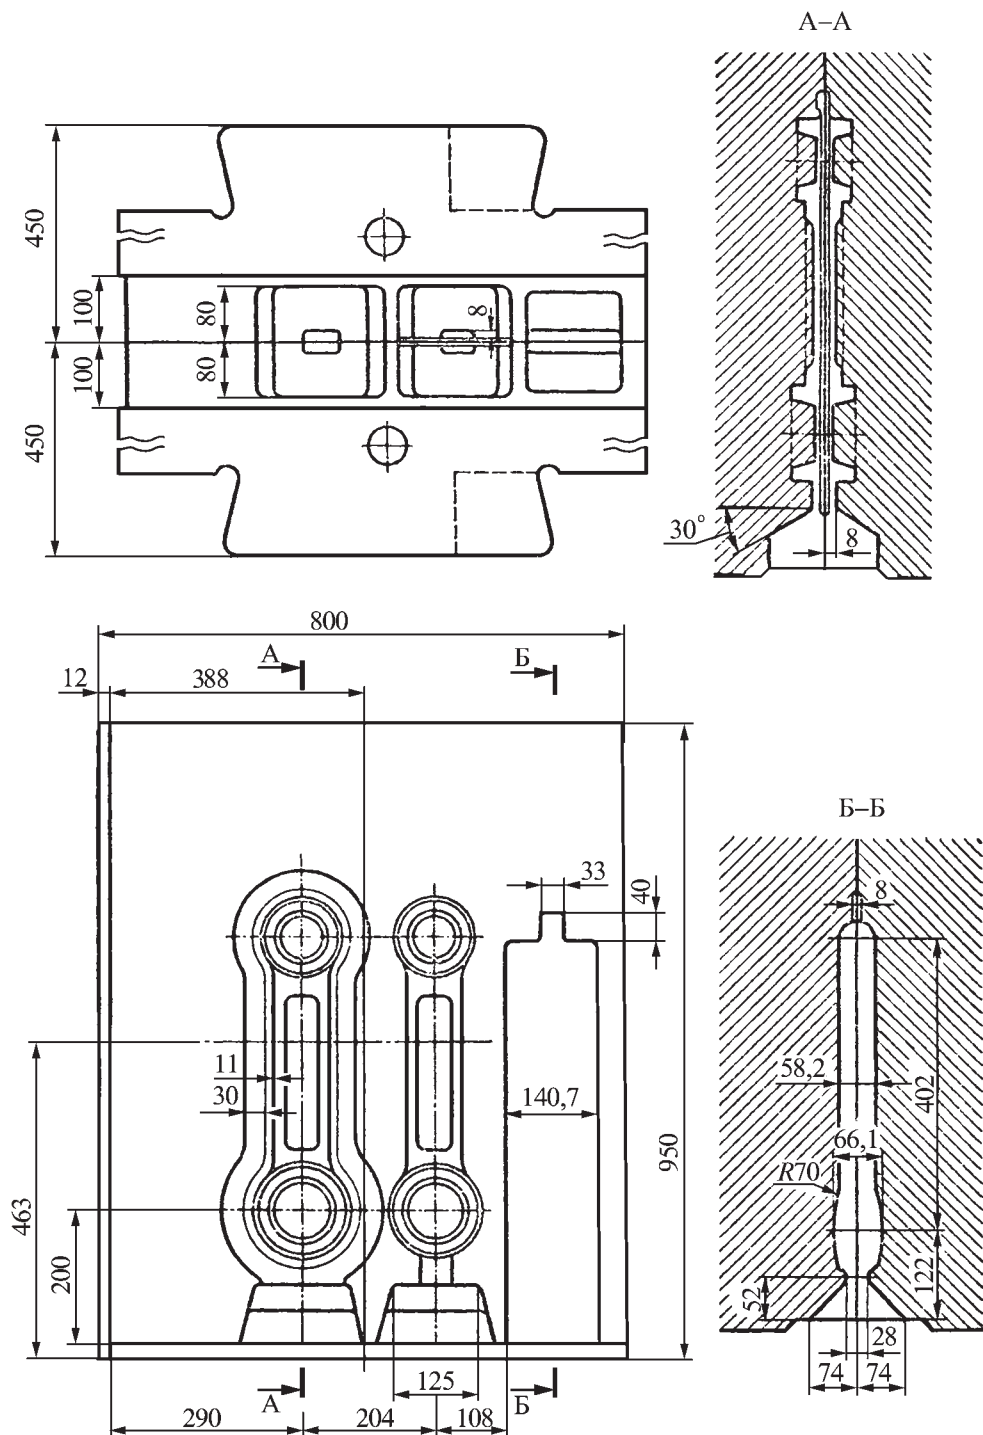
Молотовый штамп для поковки прицепного шатуна
